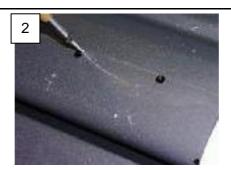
Bohrung der vorderen Befestigungspunkte / Drill the front attachment points
